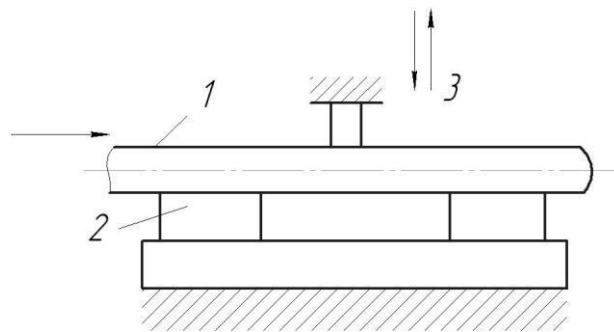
Схема одноразового пружно-пластичний вигину на правильному пресі: 1 – труба; 2 – опорні подушки; 3 – пресовий штемпель
